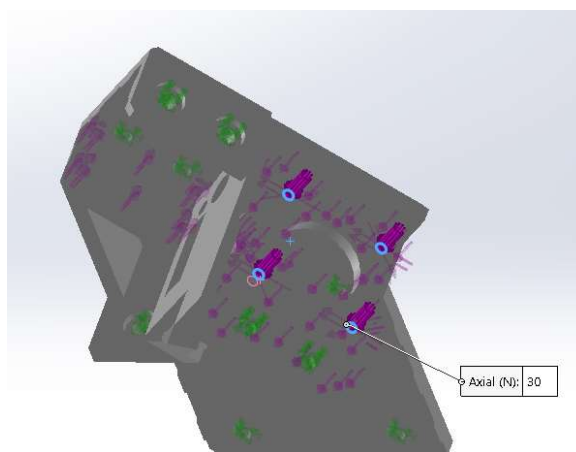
Carga axial de 30 N que sufren los tornillos del motor.
